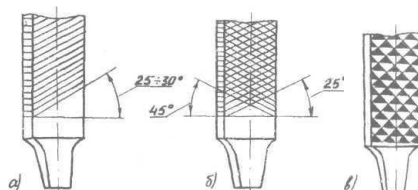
Виды насечек напильников: а) одинарная, б) двойная, в) рашпильная.
